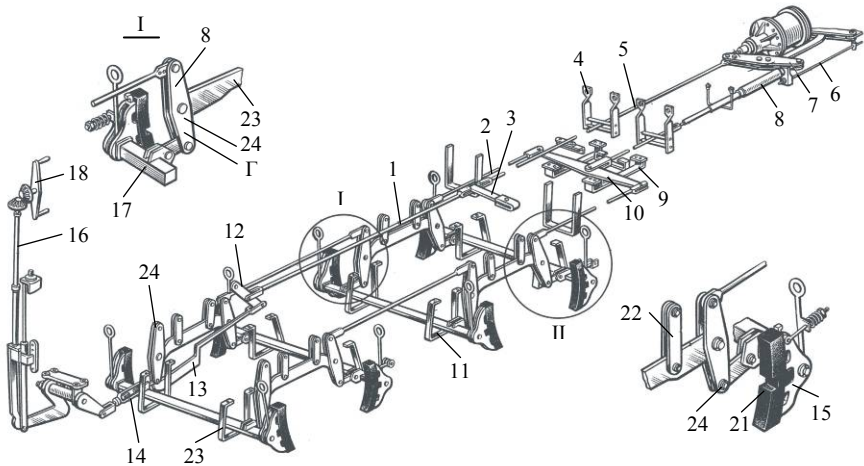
Конструкция тормозной рычажной передачи пассажирского вагона: 1 – горизонтальная тяга; 2 – тяга автоматическая тормоза; 3 – рычаг ручного тормоза; 4 – предохранительная скоба тяги; 5 – тяга ручного тормоза; 6 – тяга стержневого привода авторегулятора; 7 – горизонтальный рычаг; 8 – авторегулятор; 9 – предохранительная скоба; 10 – промежуточный рычаг; 11 – предохранительная скоба траверсы; 12 – рычаг; 13 – подосная тяга ручного тормоза; 14 – стяжная муфта; 15 – башмак тормозной колодки; 16 – винт ручного тормоза; 17 – траверса; 18 – рукоятка привода ручного тормоза; 19 – пружинный фиксатор колодки; 20 – одинарная подвеска; 21 – тормозная колодка; 22 – подвеска; 23 – затяжка вертикальных рычагов; 24 – вертикальный рычаг
